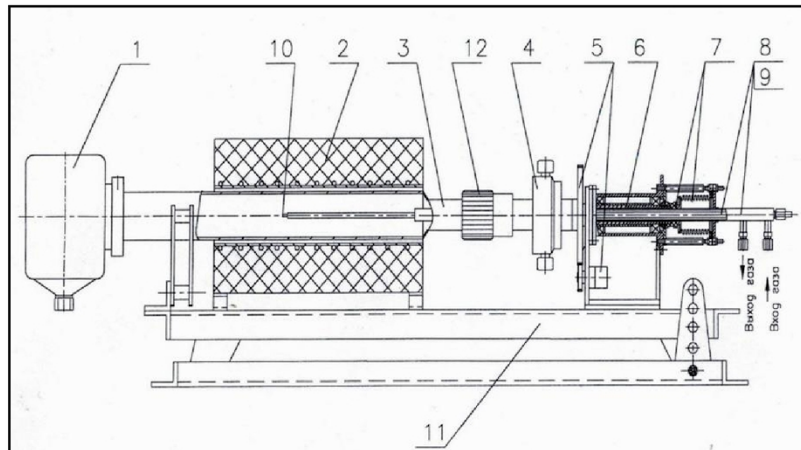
Схема установки с вращающимся реактором для получения водорода и углеродных наноструктур: 1 – приемная емкость, 2 – электропечь, 3 – корпус реактора, 4 – камера загрузки, 5 – привод (мотор-редуктор, зубчатая пара), 6 – вал полый, 7 – узел сильфонный, 8 – трубка $d=10$ мм, 9 – трубка $d=16$ мм, 10 – карман термопарный, 11 – рама, 12 – гайка.
